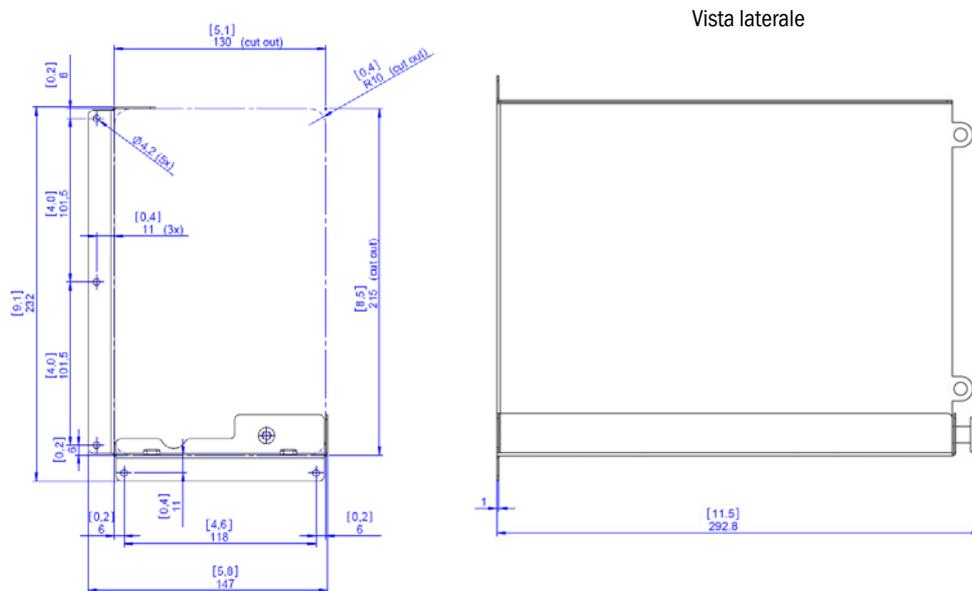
Dimensioni della staffa per montaggio a parete del Flow-X/P
